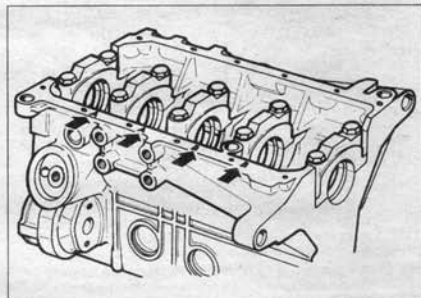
Маркировка размерного класса цилиндров на блоке
